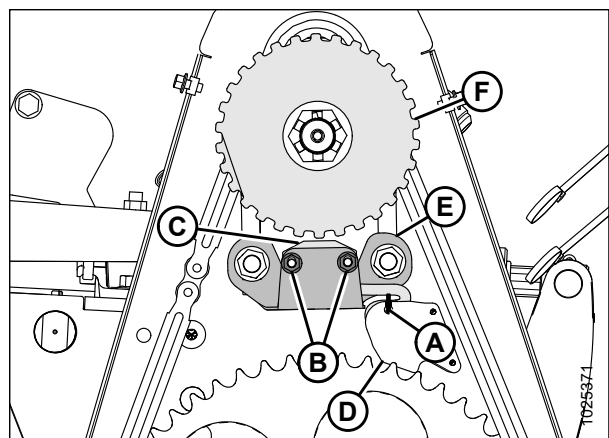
Haspelantriebsbaugruppe – Drehzahlsensor
